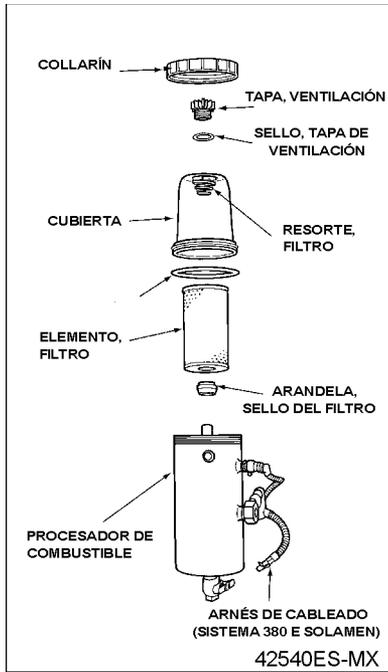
Ensamble del Procesador de Combustible de Davco 382E Fuel Pro
